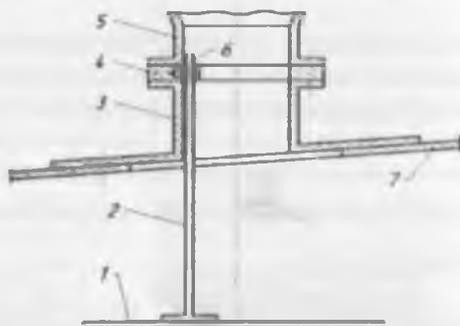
Диск-отражатель: 1 – диск; 2 – стойка; 3 – монтажный патрубок; 4 – фланец; 5 – дыхательный клапан; 6 – болт для крепления стойки к фланцу; 7 – крыша резервуара
